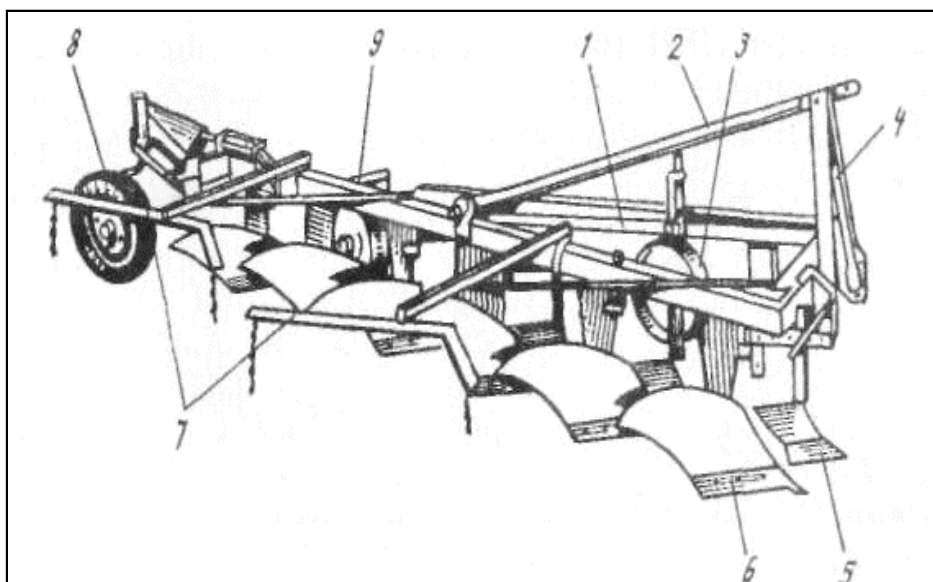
Плуг ПЛП-6-35: 1 – рама; 2 – догрузатель; 3 – полевое колесо; 4 – устройство для навешивания плуга; 5 – предплужник; 6 – корпус; 7 – устройство для присоединения борон; 8 – бороздовое колесо; 9 – дисковый нож
